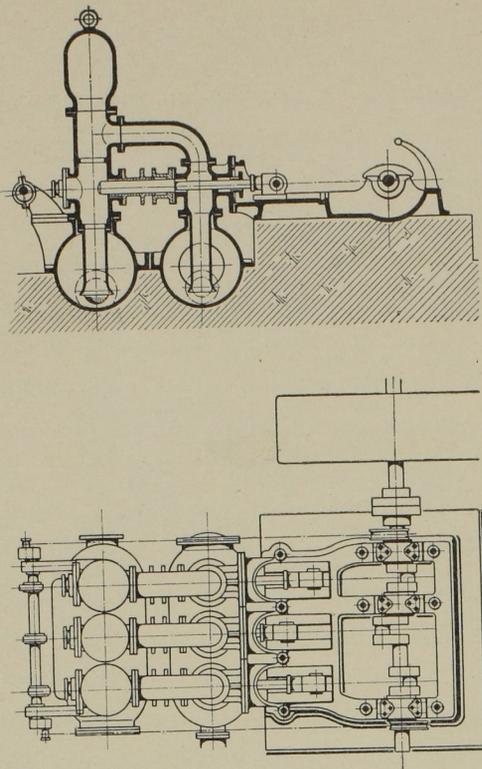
Entwurf einer raschlaufenden Pumpe für Leopoldshall.
